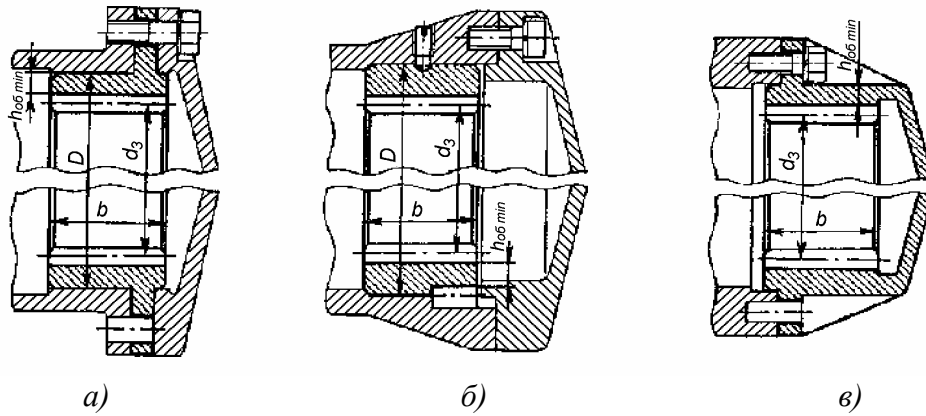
Неплавающие невращающиеся центральные колеса с внутренними зубьями
